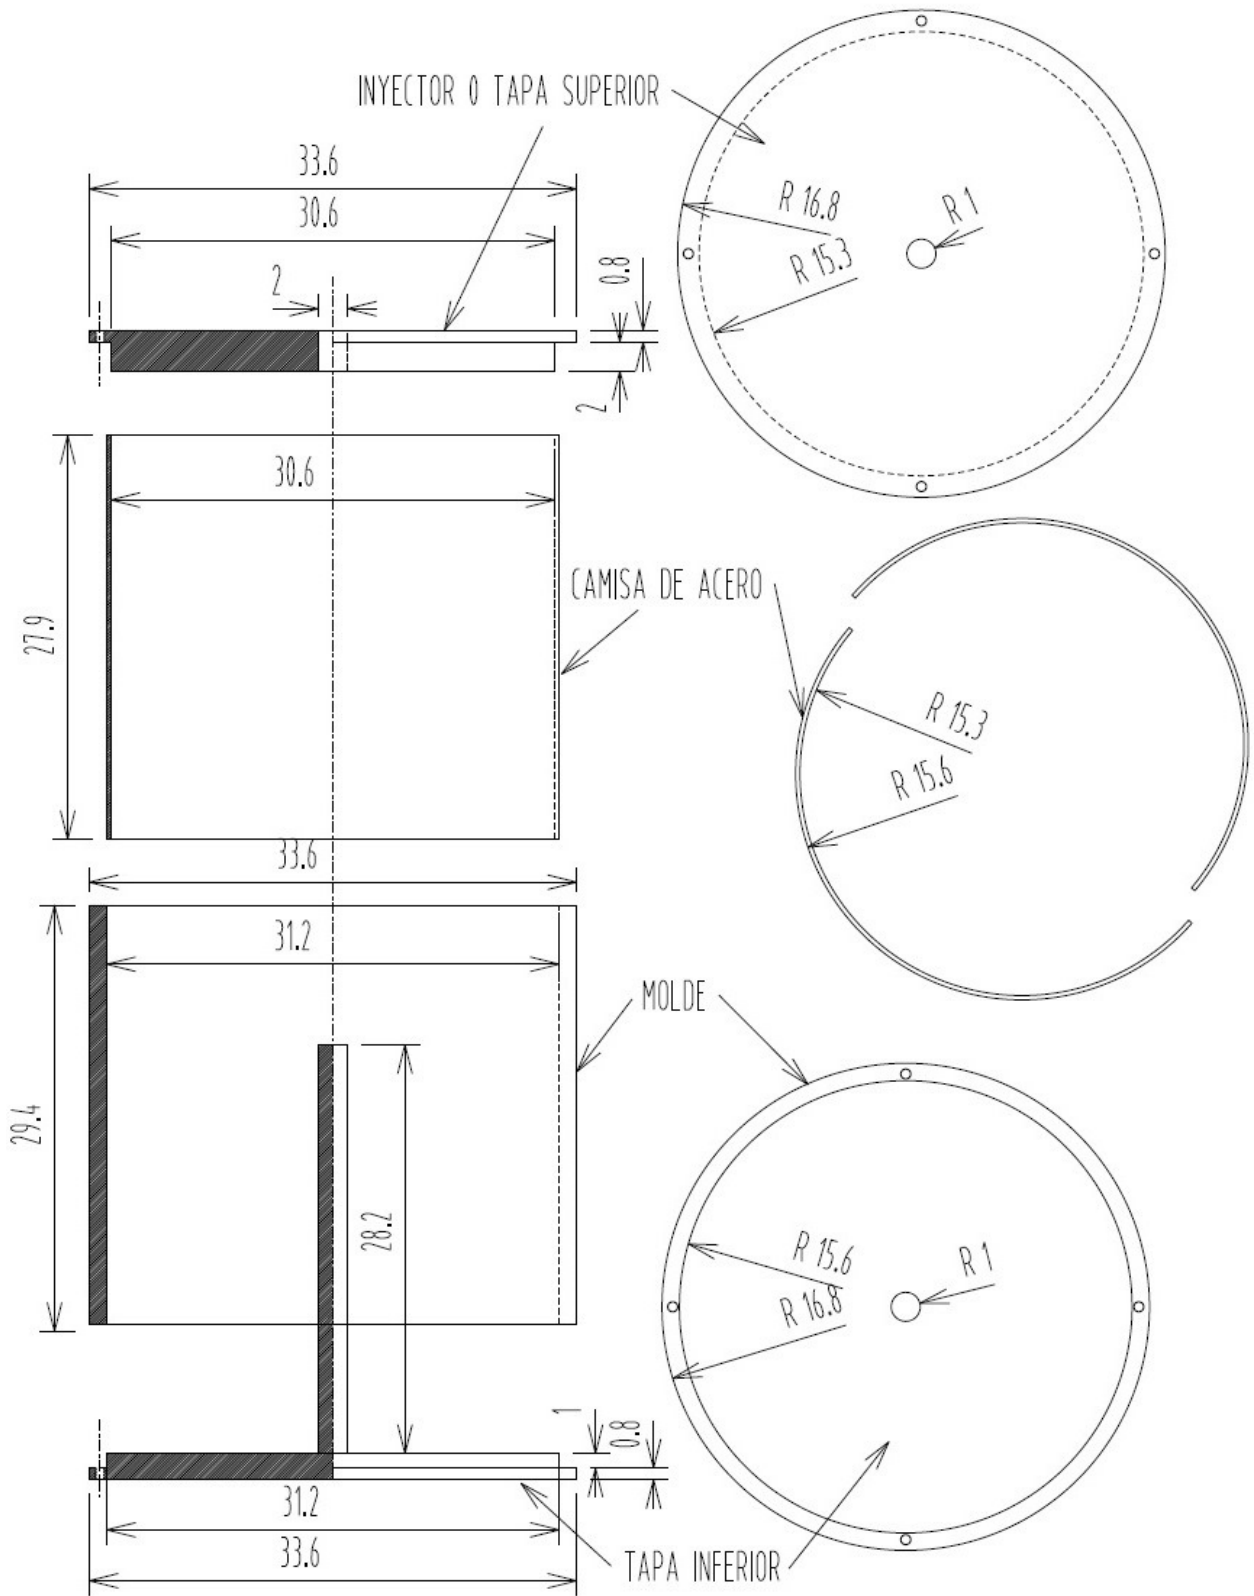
, Componentes de Molde de aisladores Plantas y Secciones en vista y corte.(dim. en cm)
